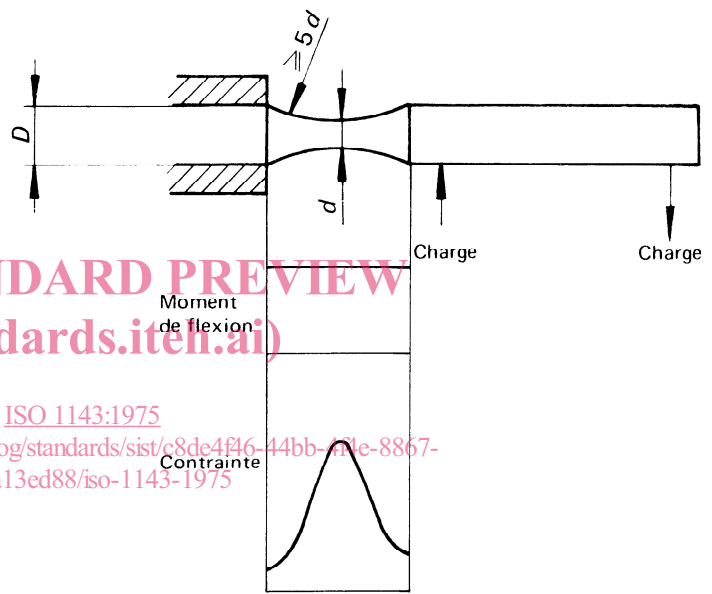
Éprouvette toroïdale – charge appliquée en deux points
